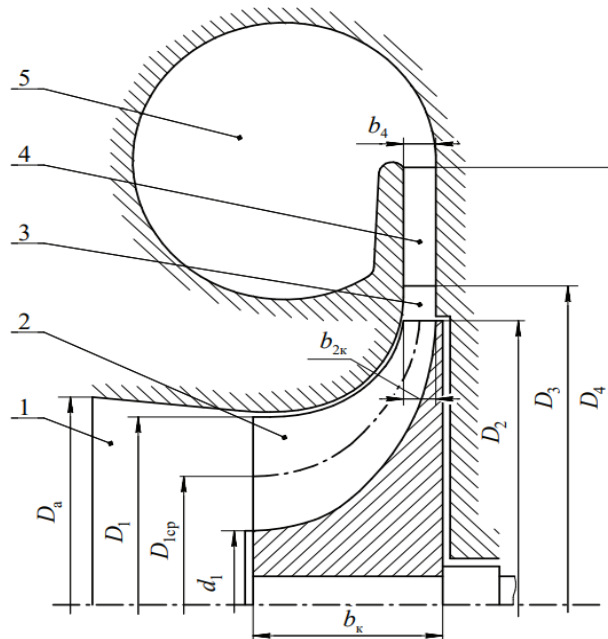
Схема проточної частини компресора: 1 – вхідний пристрій; 2 – робоче колесо; 3 – безлопатковий дифузор; 4 – лопатковий дифузор; 5 – повітрозбірник
